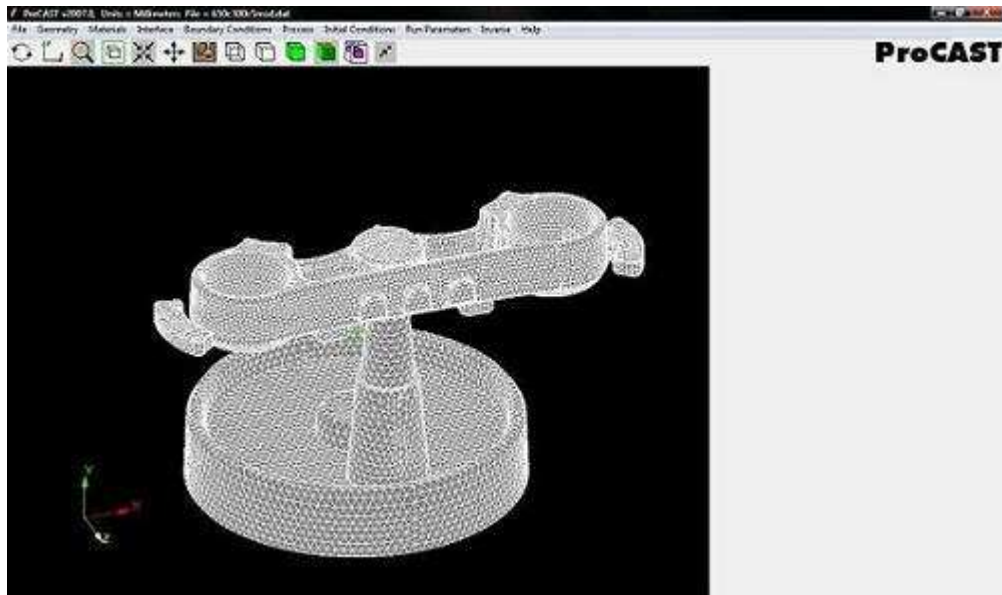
Imagen de la malla generada con el módulo PreCAST
